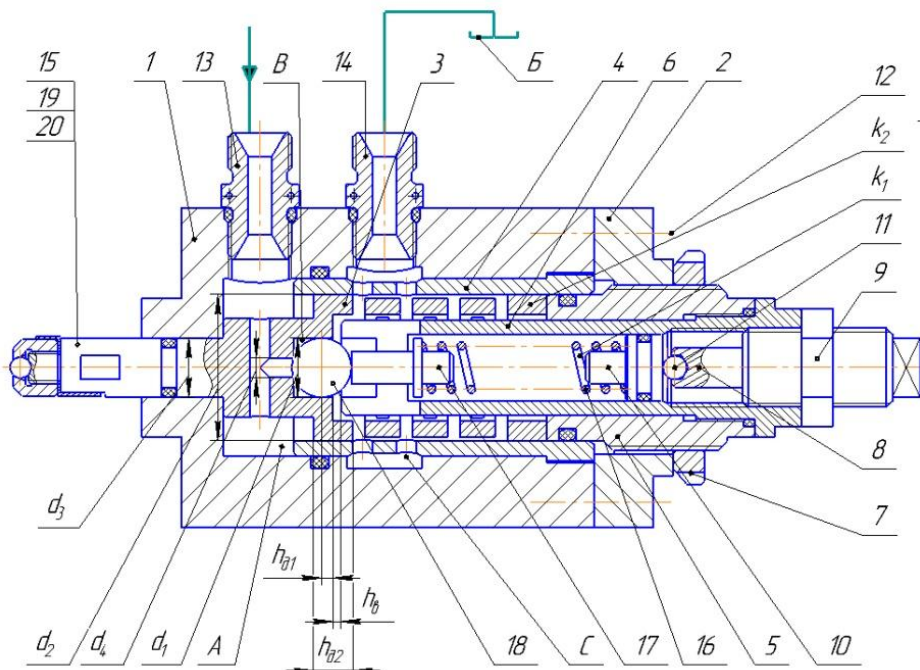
Конструкція гідроімпульсного пристрою для ППД поверхонь металевих деталей з силовою ланкою, суміщеною з прорізною пружиною
